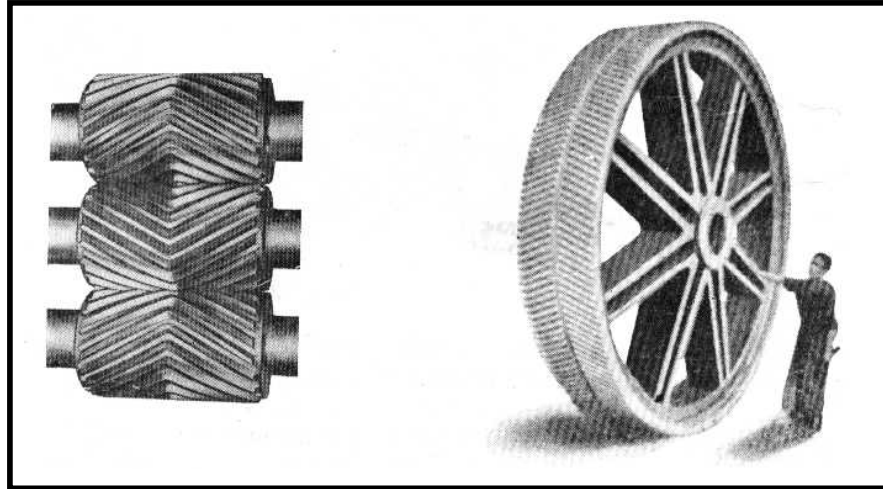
ENGRANAJES DOBLE HELICOIDALES
